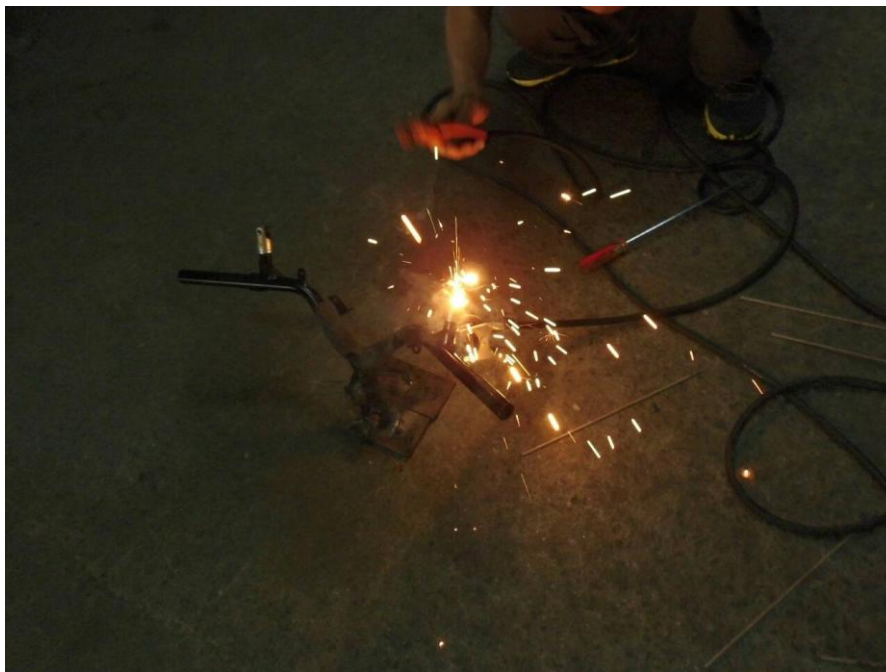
焊接伸縮棒與萬向接頭
